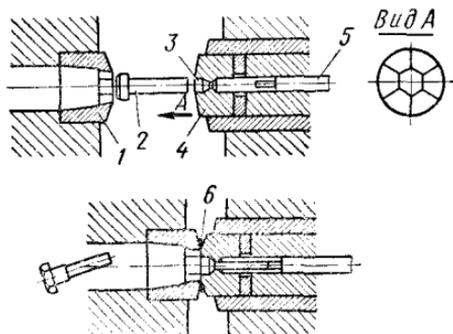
Схема обрезки граней головки болта и выдавливания его стержня под накатку резьбы
